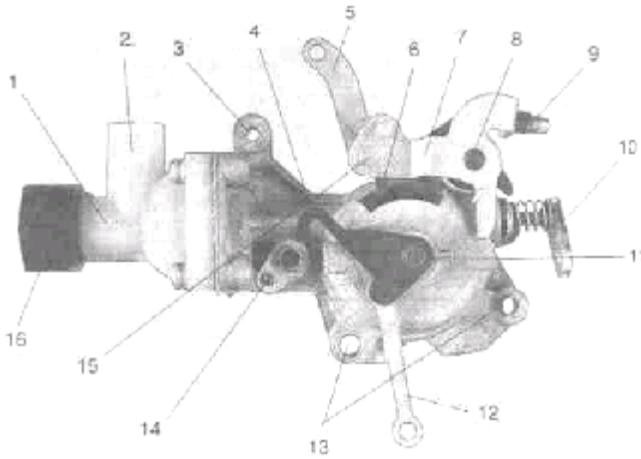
Вид сзади на снятый с карбюратора корпус автоматического пускового устройства (вариант исполнения без рычага блокировки открытия дроссельной заслонки вторичной камеры):
